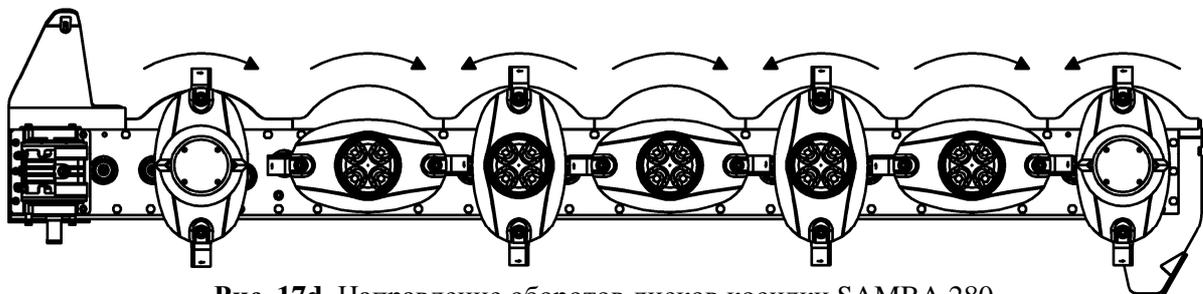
Направление оборотов дисков косилки SAMBA 280
